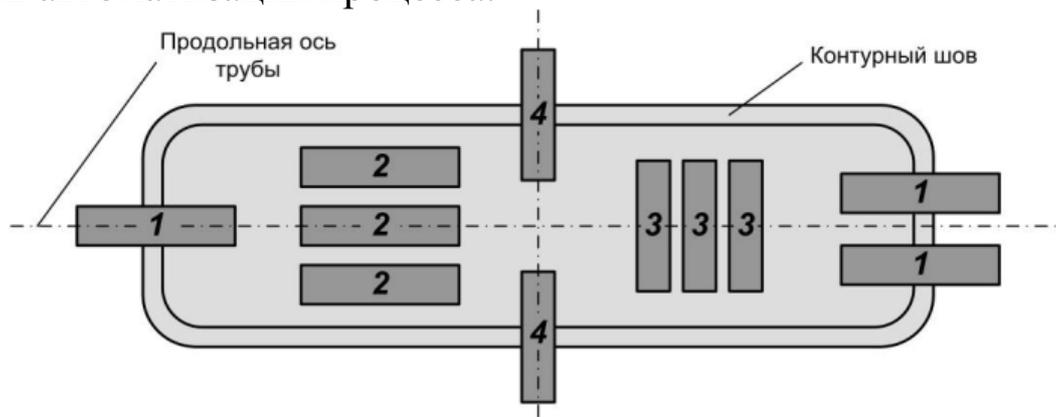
Схема вырезки образцов для механических испытаний (1 – статическое растяжение; 2 – статический изгиб; 3 – ударный изгиб; 4 – твердость)
